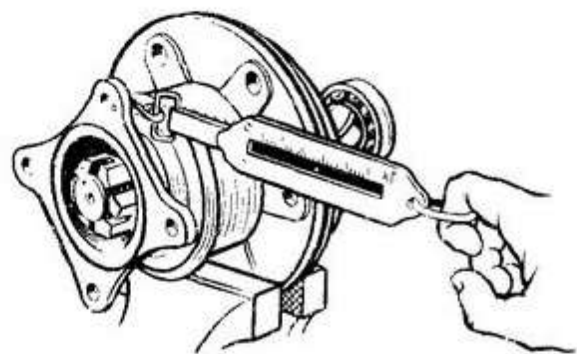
Проверка затяжки подшипников ведущей шестерни
